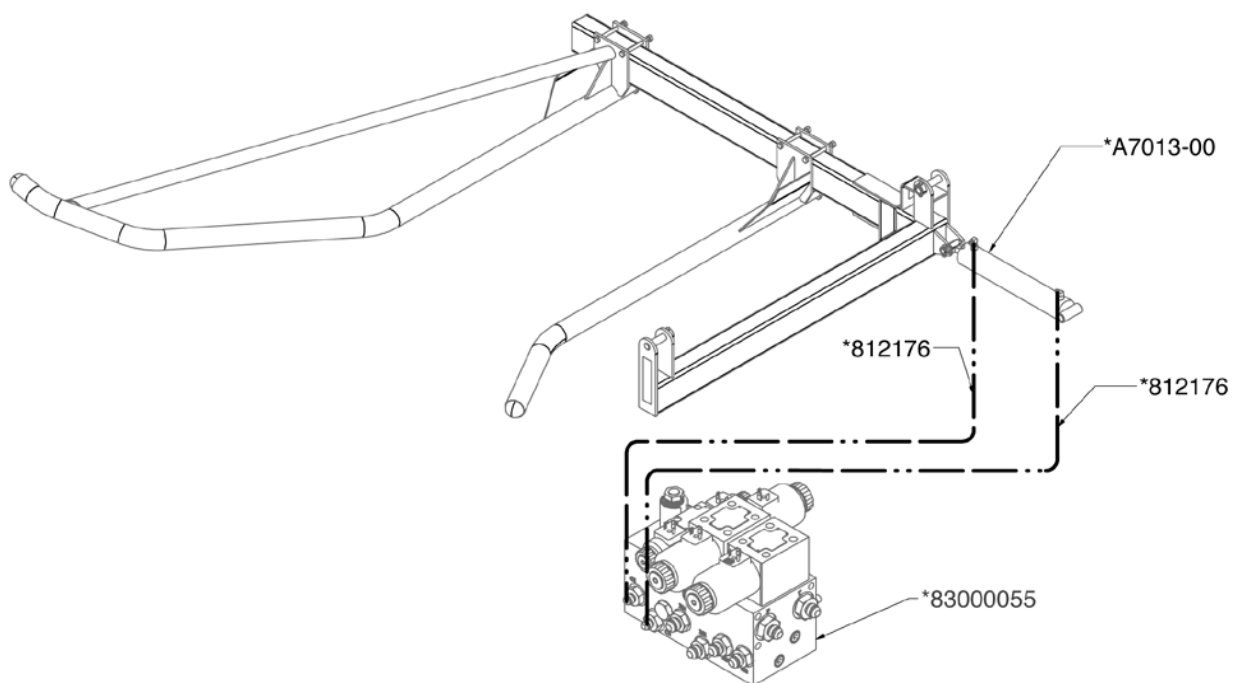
Чертеж сборки гидравлики зафиксированного загрузочного захвата
